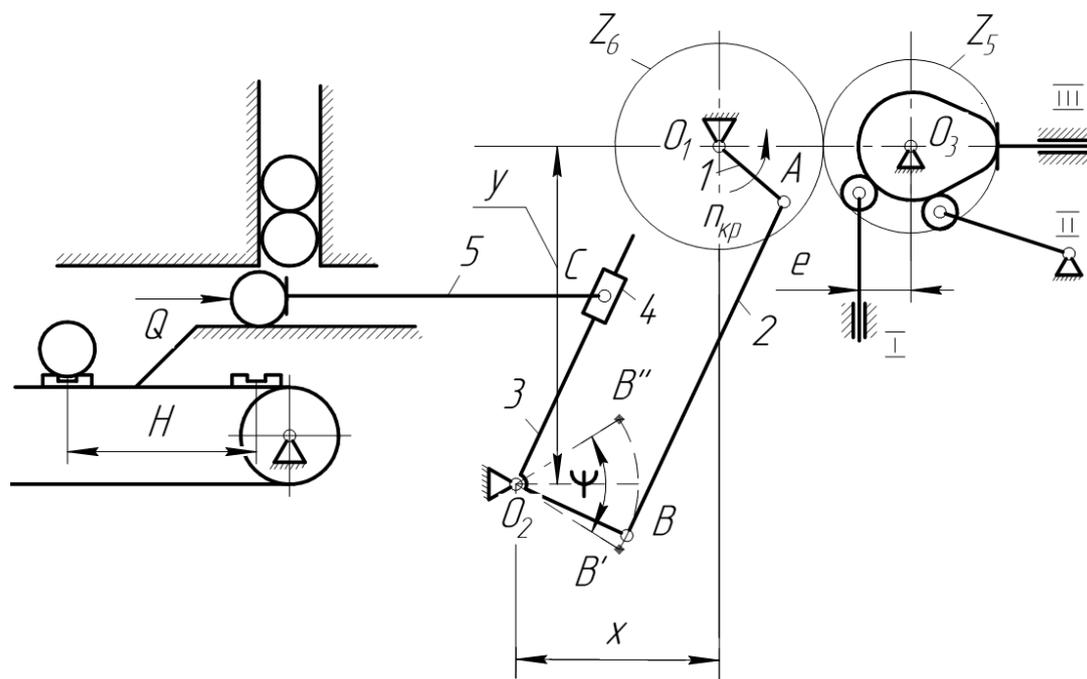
Механизм устройства подачи деталей из накопителя
